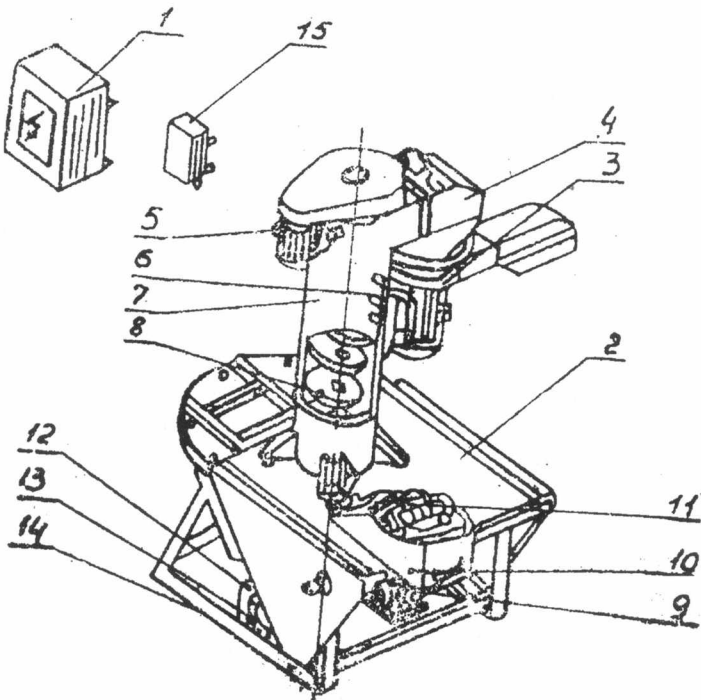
Подрібнювач коренебульбоплодів ИКМ-Ф-10: 1 - шкаф управління; 2 - ванна; 3 - подрібнювач; 4 - кришка; 5 - електродвигун; 6 - патрубок; 7 - корпус шнека; 8 - шнек; 9 - мотор-редуктор; 10 - кожух; 11 - транспортер; 12 - кожухтранспортера; 13 - ніж; 14 - рама; 15 - обладнання захисного відключення.
